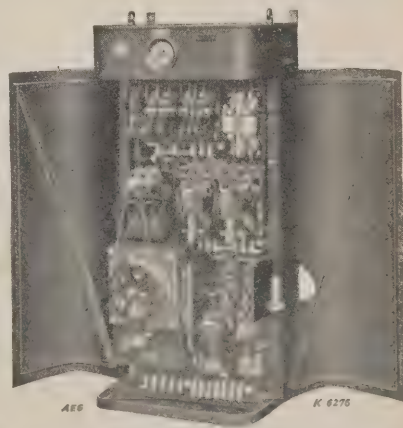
Selbsttätiger Umkehr-Regulier-Anlasser einer Universal-Drehbank-Druckknopfsteuerung. (Türen geöffnet.)
